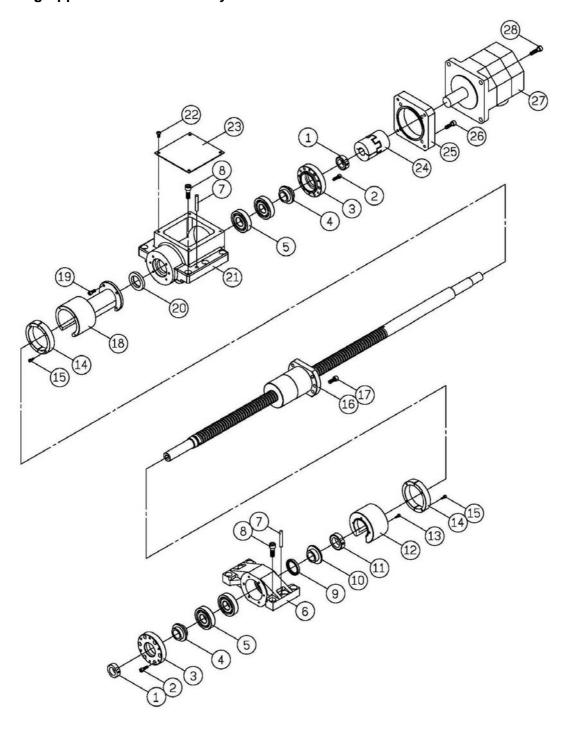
Baugruppe Y-Achse - Assembly Y-Axis
